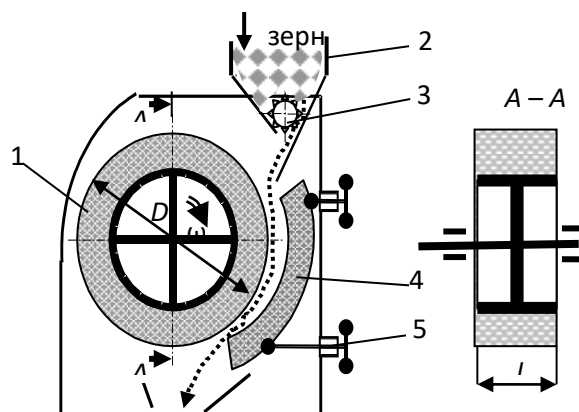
Приципова схема вальцедекового верстата: 1— валок; 2 — бункер; 3 — валок живильний ; 4 — дека ; 5 — механізм регулювання деки.
